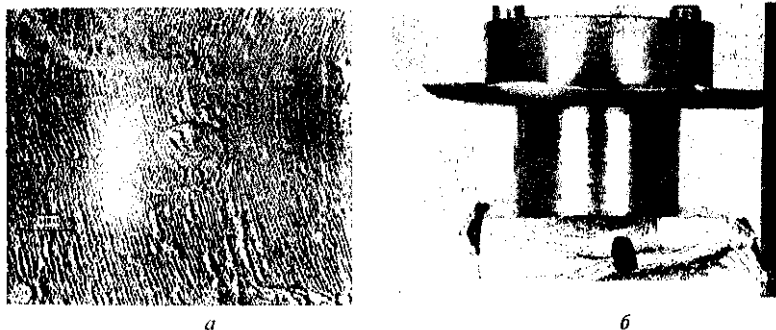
Бороздки усталости на поверхности излома сплава Al-Cu-Mg [1] — а; макроусталостные линии на поверхности излома коленчатого вала, изготовленного из стали 45, — б
